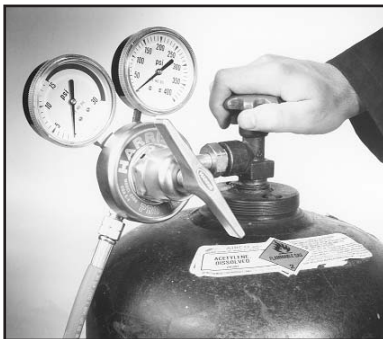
Abriendo la Valvula del Cilindro de Gas Combustible
